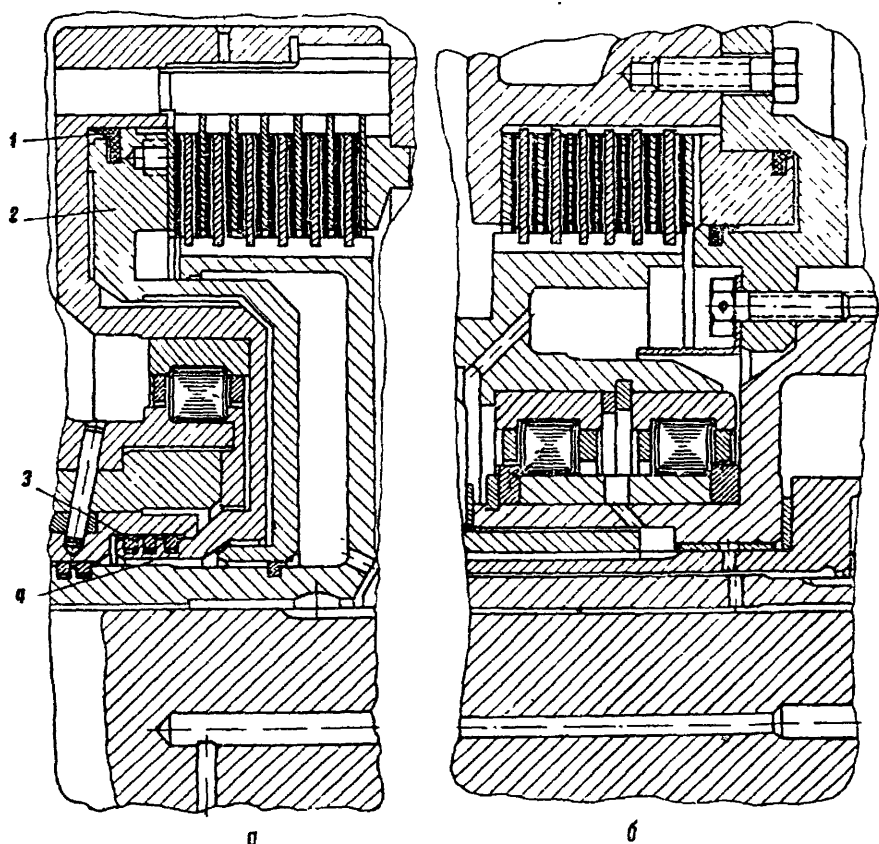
Конструкция кольцевых сервомоторов гидромеханической коробки передач
